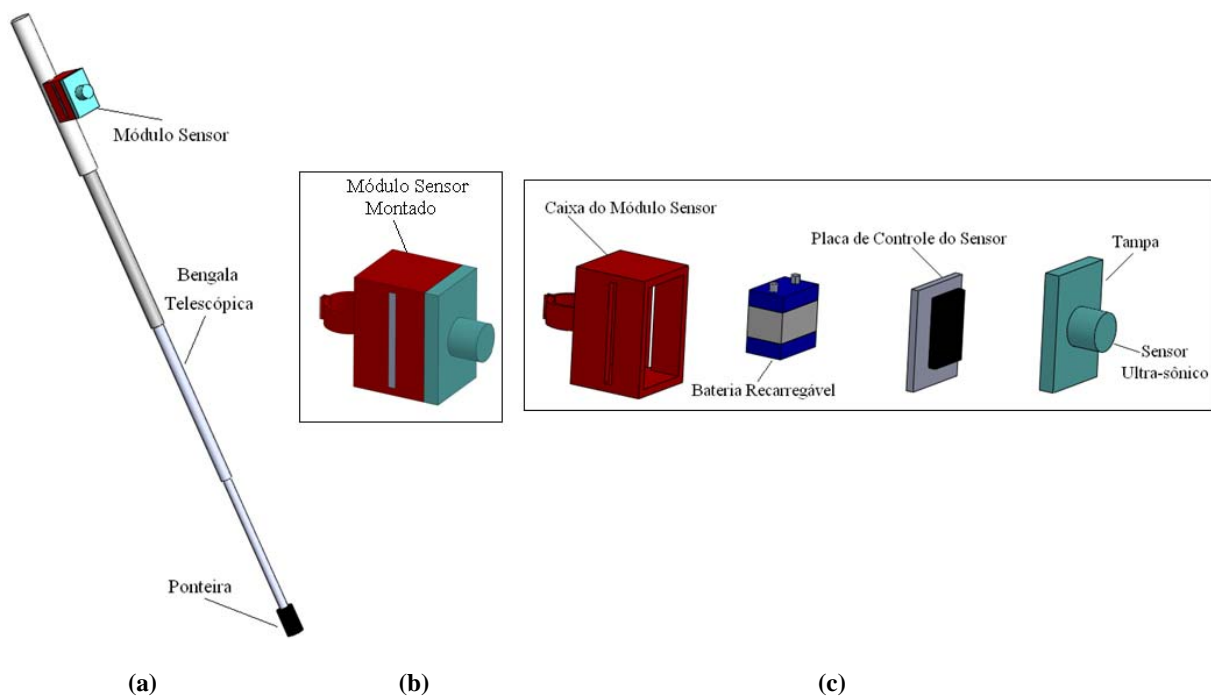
(a) Bengala Eletrônica Telescópica; (b) Módulo Sensor; (c) Vista explodida do Módulo Sensor.
